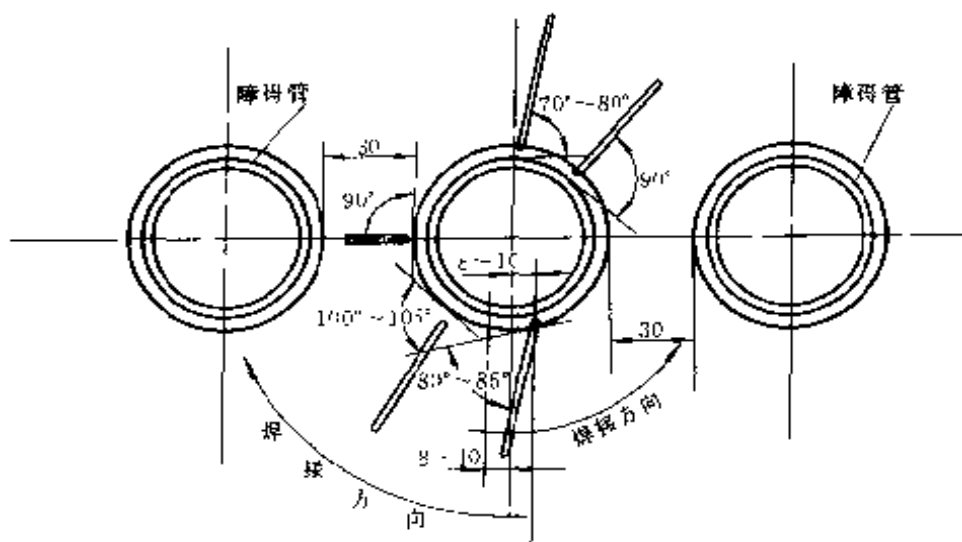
管对接水平固定障碍焊焊条电弧焊盖面层焊接的焊条角度
